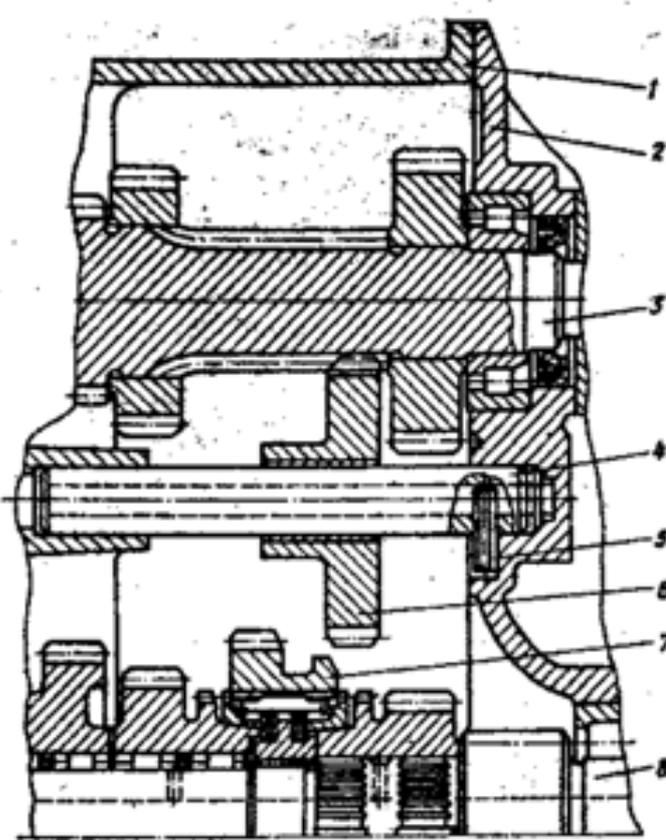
Промежуточная шестерня заднего хода коробки передач: 1 - картер коробки; 2 - картер сцепления; 3 - ведущий вал; 4 - ось промежуточной шестерни заднего хода; 5 - штифт; 6 - шестерня промежуточная заднего хода; 7 - шестерня ведомая заднего хода; 8 - ведущая шестерня главной передачи
